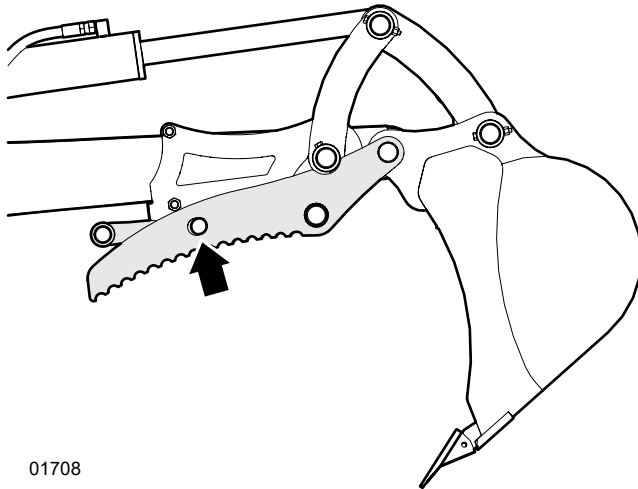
Emplacement des trous arrière de l'écrou mécanosoudé et du support du pouce mécanique
